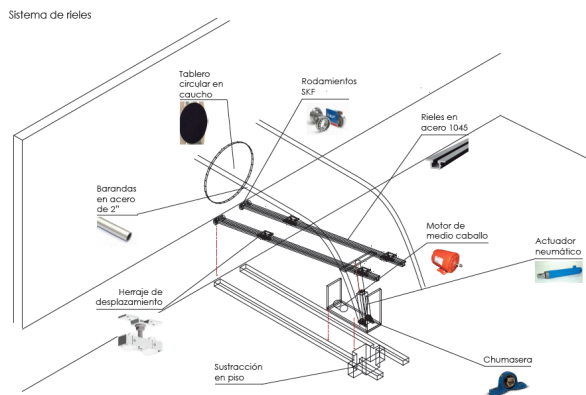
Detalle constructivo sistema de rieles. Autoría propia. Pág: 93
